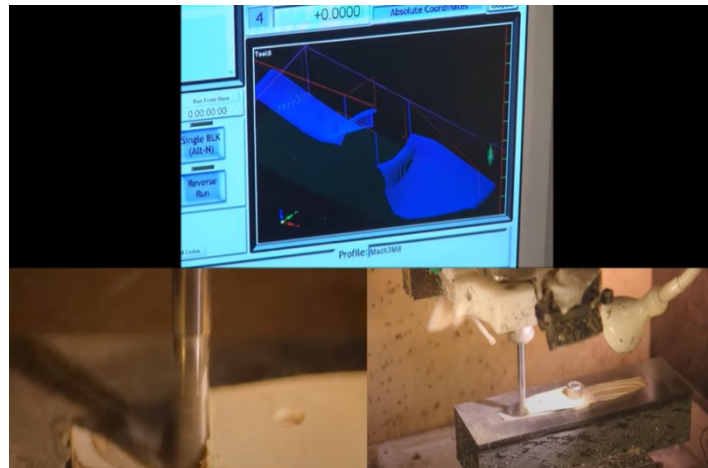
Proceso de modelado de propela mediante maquinado CNC
